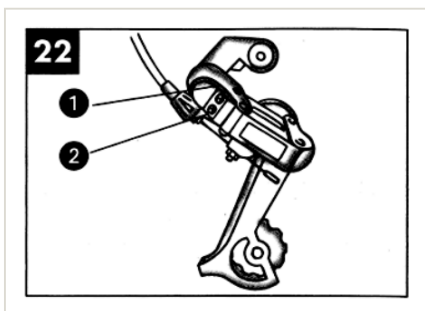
Hinteres Schaltwerk: 1 Schraube a · 2 Schraube b
